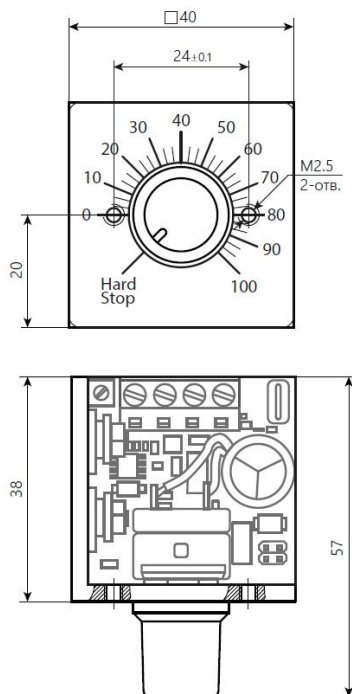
Габаритные и присоединительные размеры блока БУКД-12
